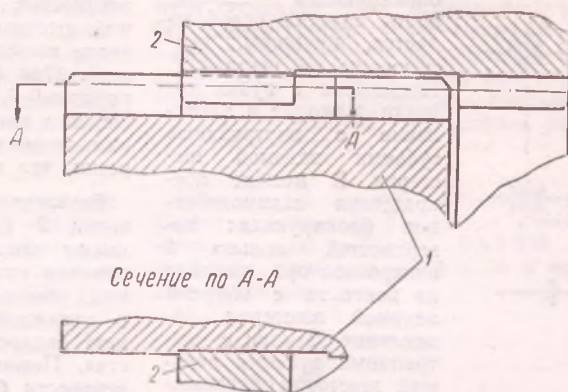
Блокировка, препятствующая выключению передачи без сцепления:
